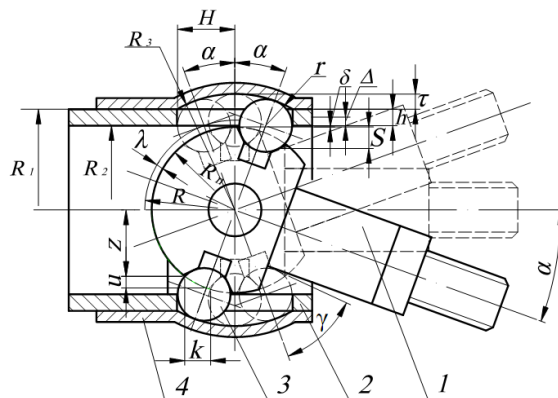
Розрахункова схема конструкції шарнірного з'єднання гвинтового робочого органу
